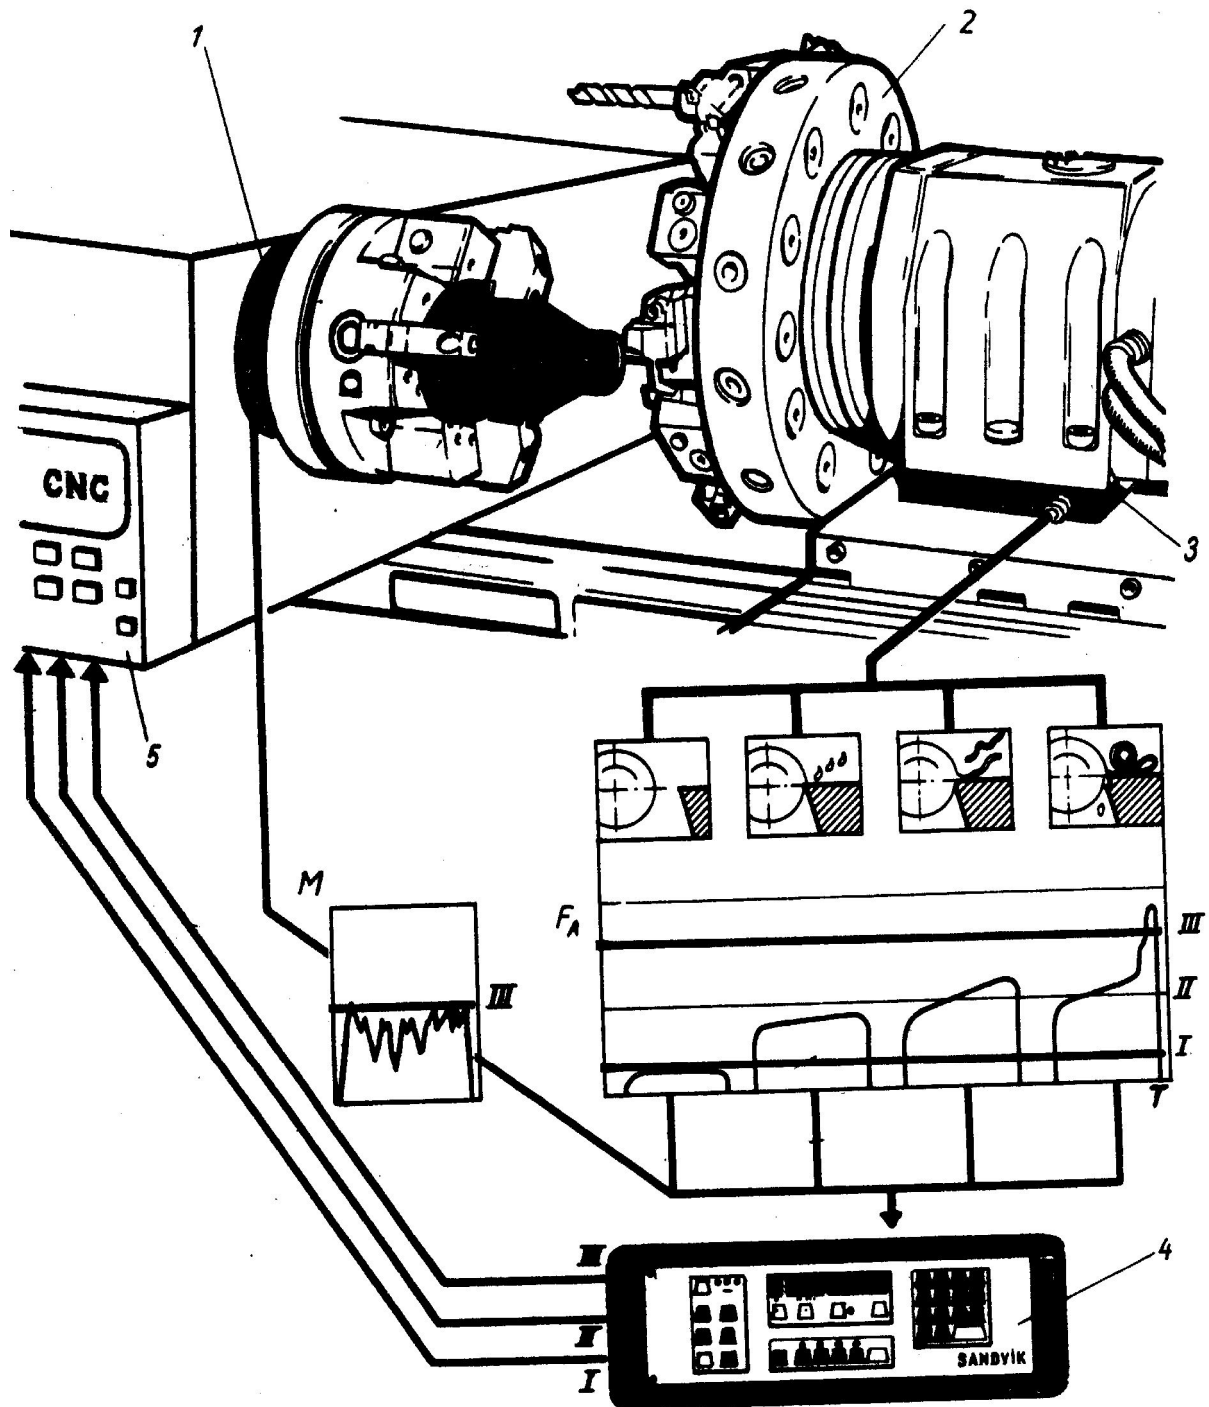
Схема діагностування ріжучого інструмента на токарно-револьверному верстаті з ЧПК: 1 — датчик обертального моменту  $M$ ; 2 — револьверная головка; 3 — датчик осьового зусилля  $F_a$ ; 4 — пристрій контролю інструмента; 5 — ПЧПК
